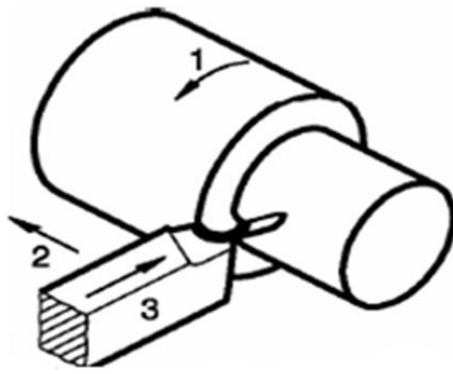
Representação dos movimentos de corte, avanço e penetração.
